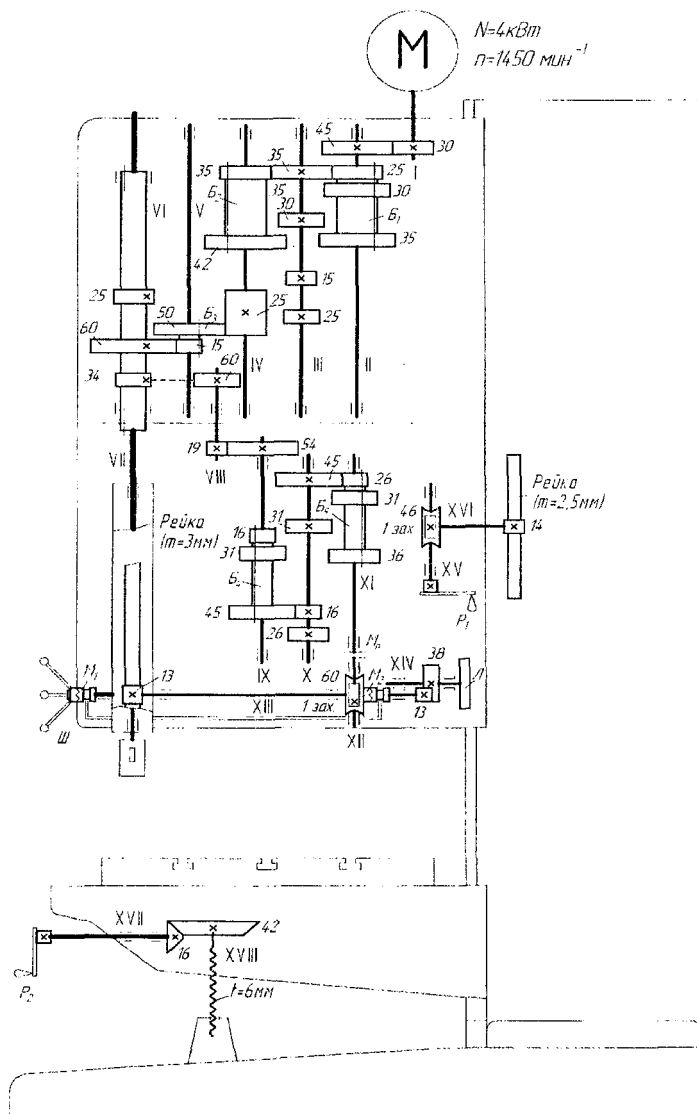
Кинематическая схема вертикально – сверлильного станка модели 2Н135.
